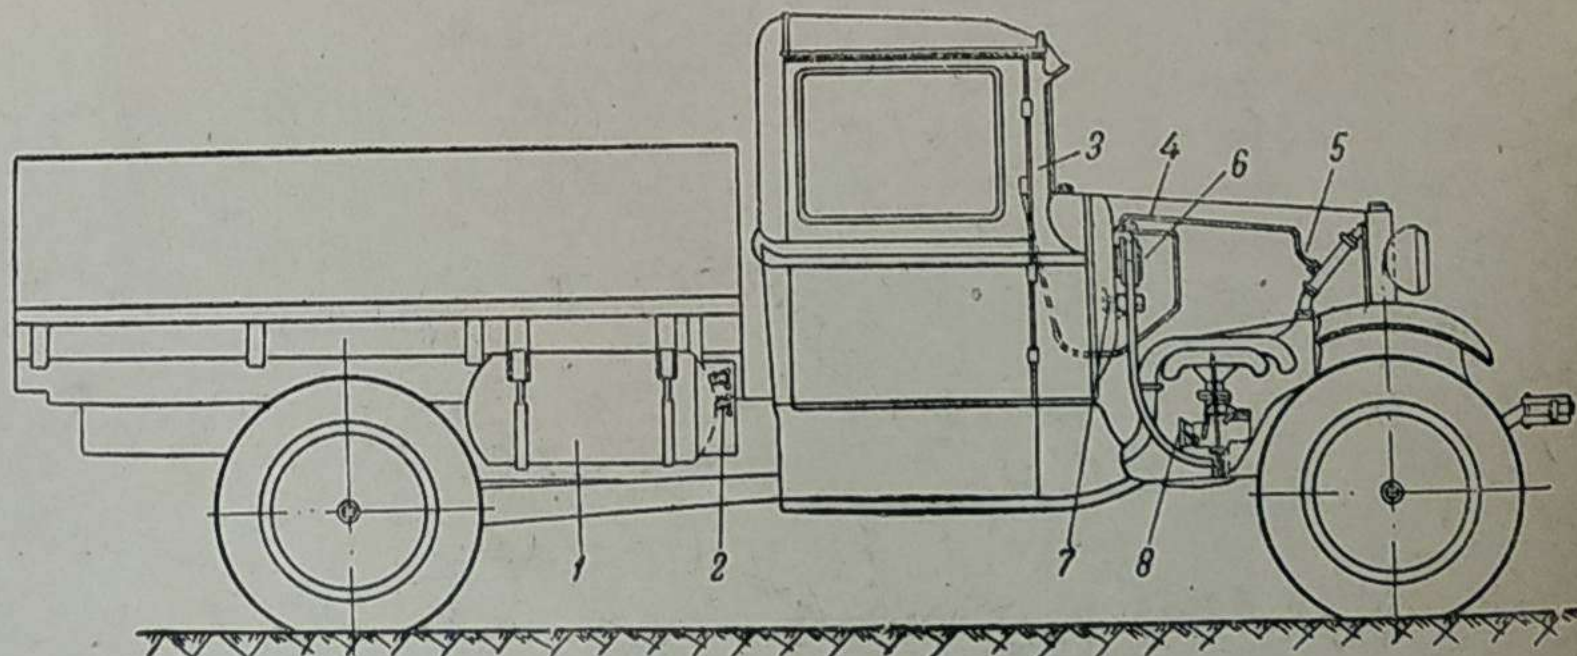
Общий вид газобаллонного автомобиля ГАЗ-45, работающего на сжиженном газе: 1 — баллон для сжиженного газа; 2 — арматура баллона; 3 — манометр; 4 — редуктор высокого давления — испаритель; 5 — подвод воды в испаритель; 6 — редуктор низкого давления; 7 — магистральный кран; 8 — карбюратор-смеситель.
